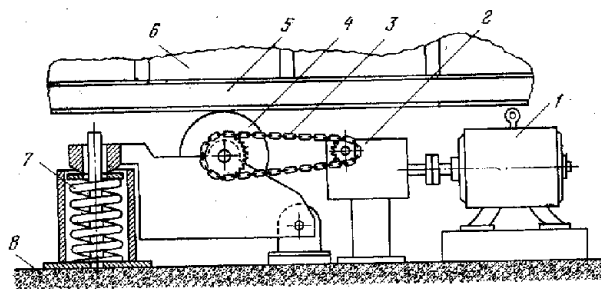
Подпружиненный ведущий каток купола. Принцип расположения соответствует рисунку 15.2, в. 1 — двигатель, 2 — редуктор, 3 — цепь, 4 — ведущий каток, 5 — кольцевая балка купола, 6 — обшивка купола, 7 — пружина, 8 — башня.
